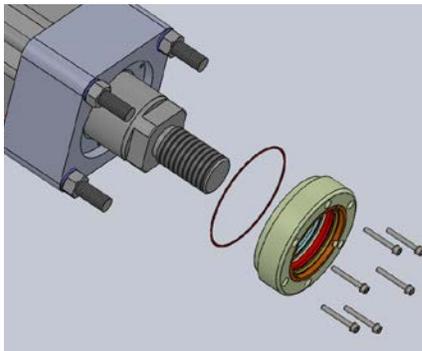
RSX-Dichtungspatrone Explosionsansicht
